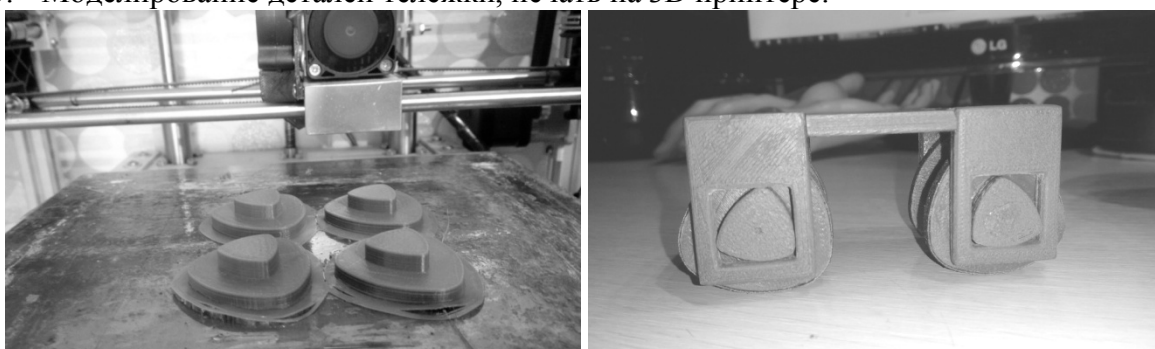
Изготовление модели тележки с колесами в форме треугольника Рёло.
